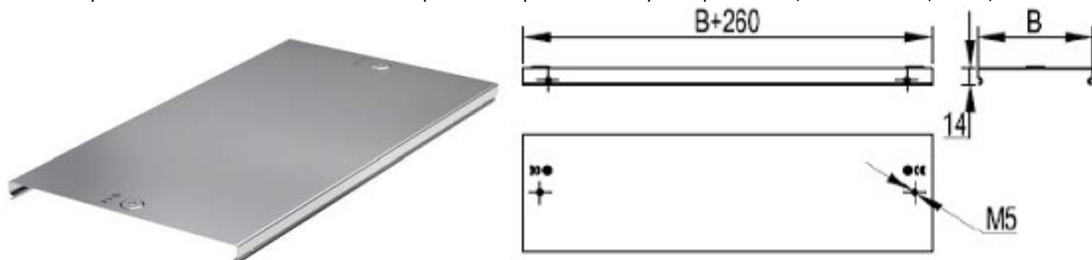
Крышка TDS на ответвитель T-образный вертикальный универсальный, тип 3832
